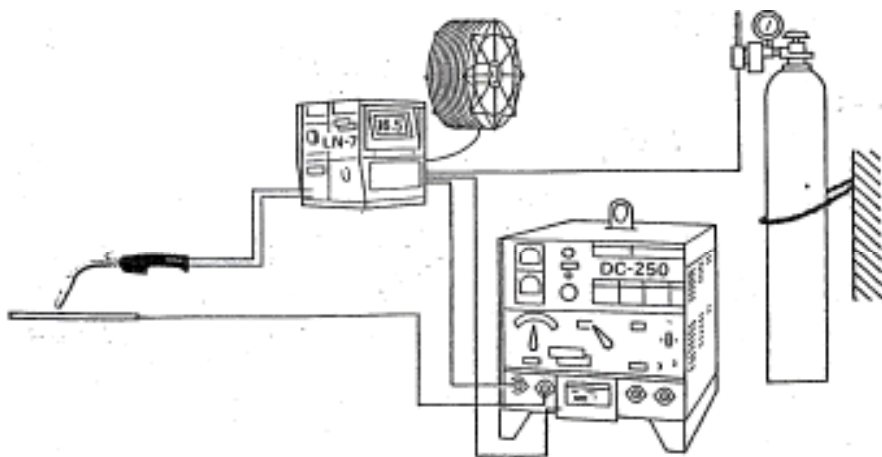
Proceso de soldadura por arco de metal y gas
